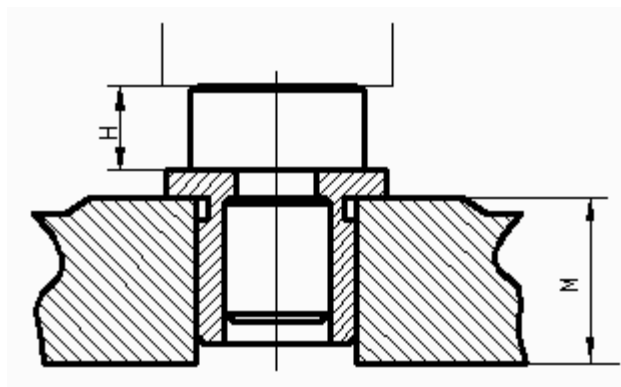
Установка опор постоянных в корпусе приспособления.
